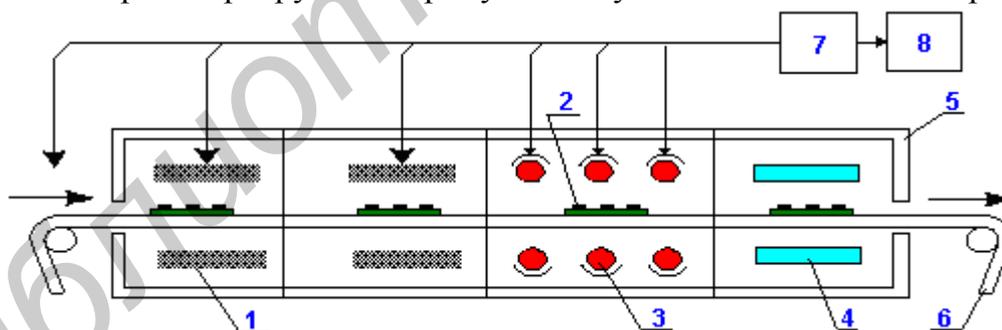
Установка ИК нагрева комбинированного типа: 1 – панельные нагреватели; 2 – печатная плата, 3 – кварцевые ИК лампы, 4 – охлаждающее устройство, 5 – корпус, 6 – конвейер, 7 – микропроцессор, 8 – дисплей
